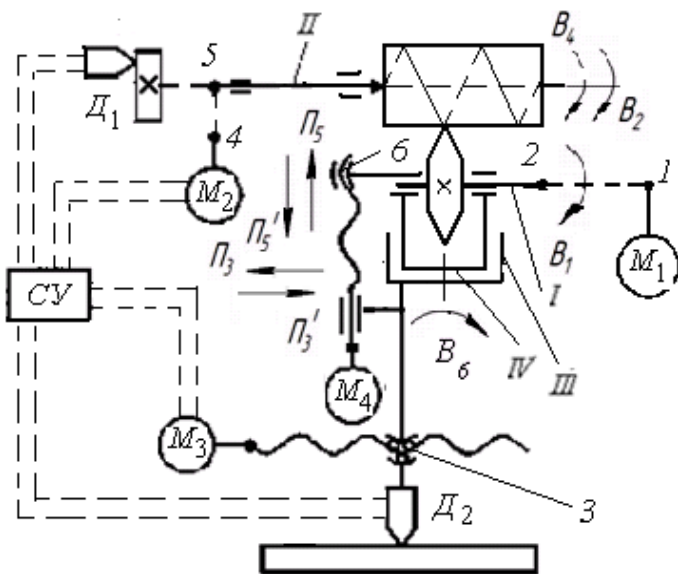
Кинематическая структура резьбофрезерного станка с мехатронными связями
